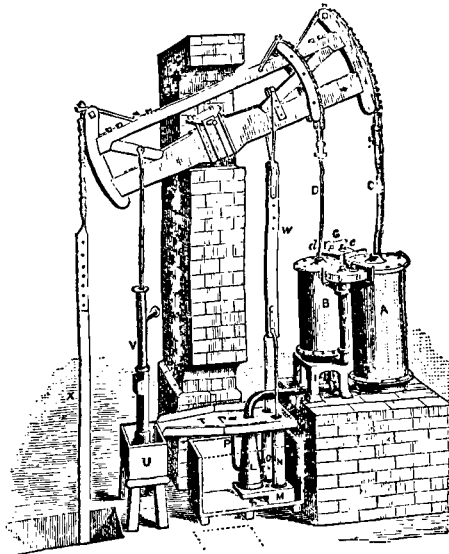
Machine à deux cylindres de Hornblower, 1781.
